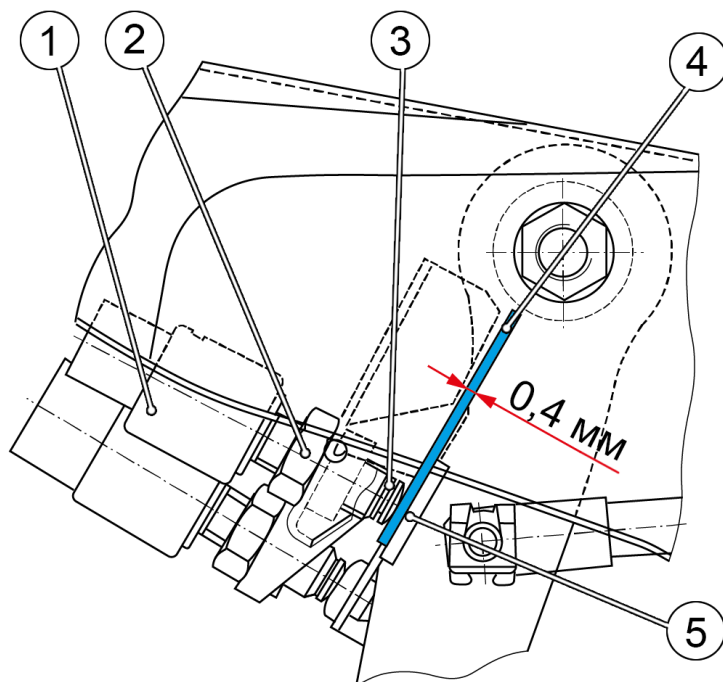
Установка выключателя сигнала торможения: 1 - выключатель сигнала торможения; 2 - стопорная гайка; 3 - головка подвижного штока выключателя; 4 - шуп; 5- опорный кронштейн педали тормоза
